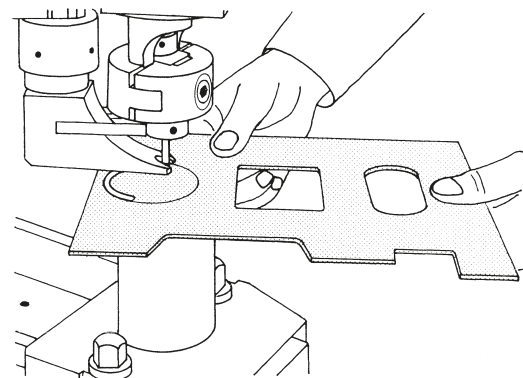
Beispiel für die Bearbeitung mit einer Nibbelmaschine
